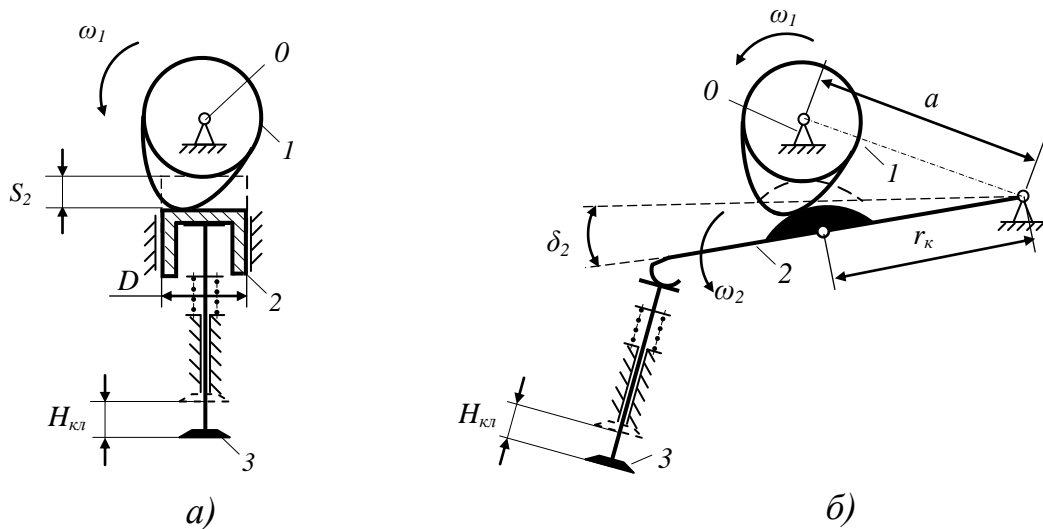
Схеми кулачкових механізмів газорозподілу високооборотних дизелів: 1 – кулачок; 2 – штовхач; 3 – клапан з комплектом клапанних пружин
